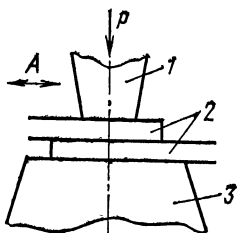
Схема процесса ультразвуковой сварки:
